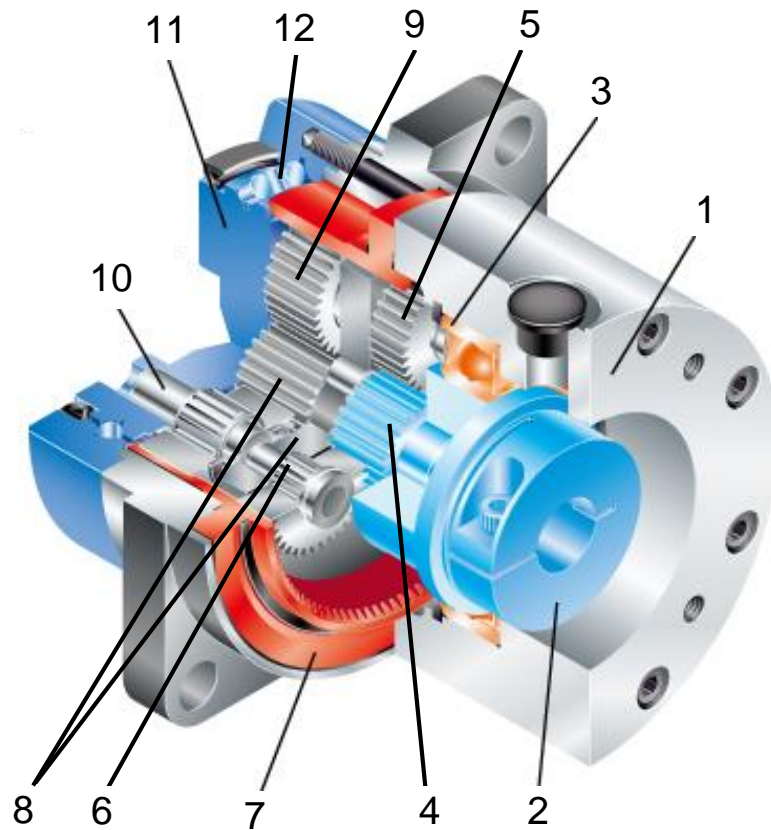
Конструкція планетарного двоступеневого редуктора стандартної серії HPG фірми Harmonic Drive Systems
